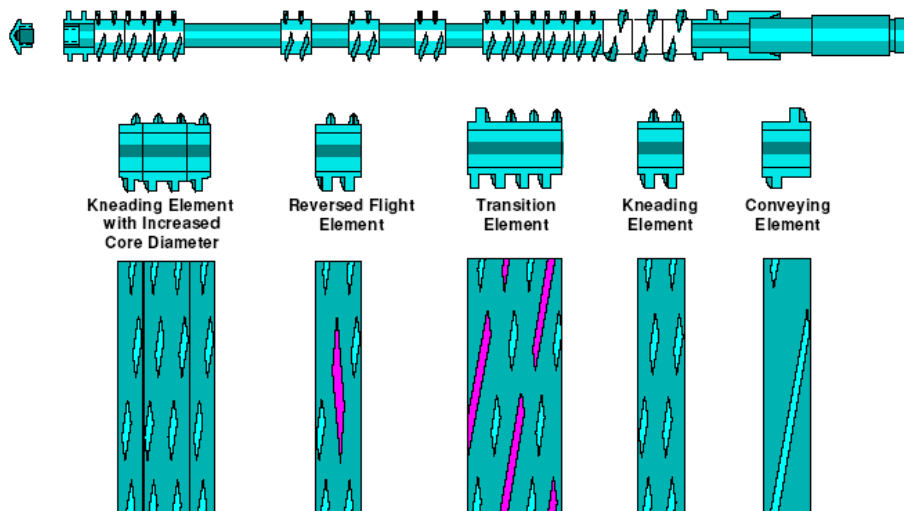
Diferentes elementos que componen un husillo de extrusión.
